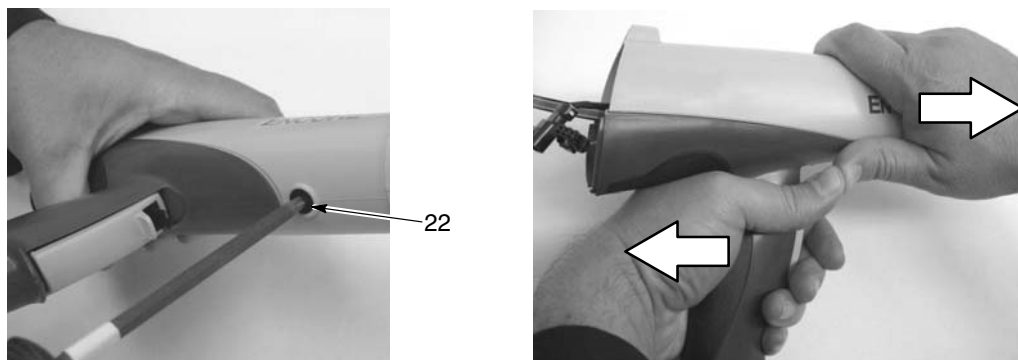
Снятие корпуса распылителя с рукоятки
